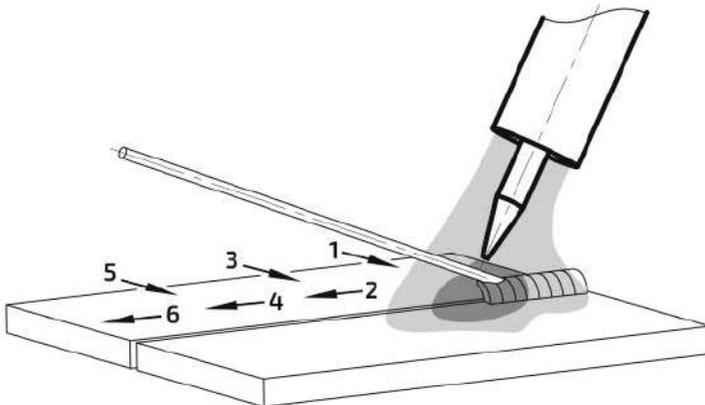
Пример манипуляции присадочной проволокой при TIG сварке.
